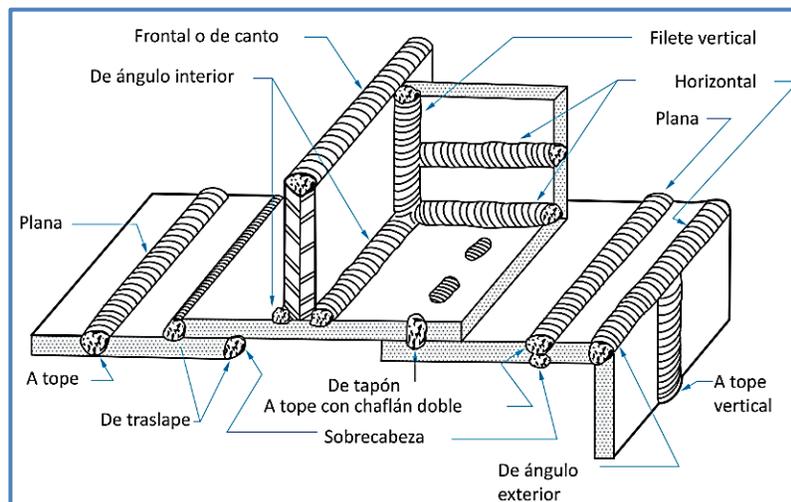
Tipos de Técnicas de soldadura por arco.
